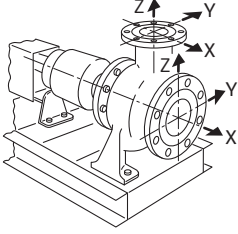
Pompa flanşlarında izin verilen kuvvetler ve momentler – pik döküm pompa
